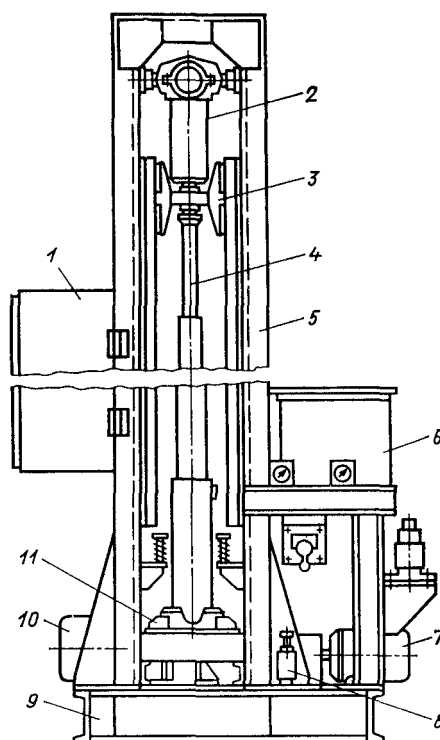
Стенд для испытания гидроцилиндра (модель С416-392)
